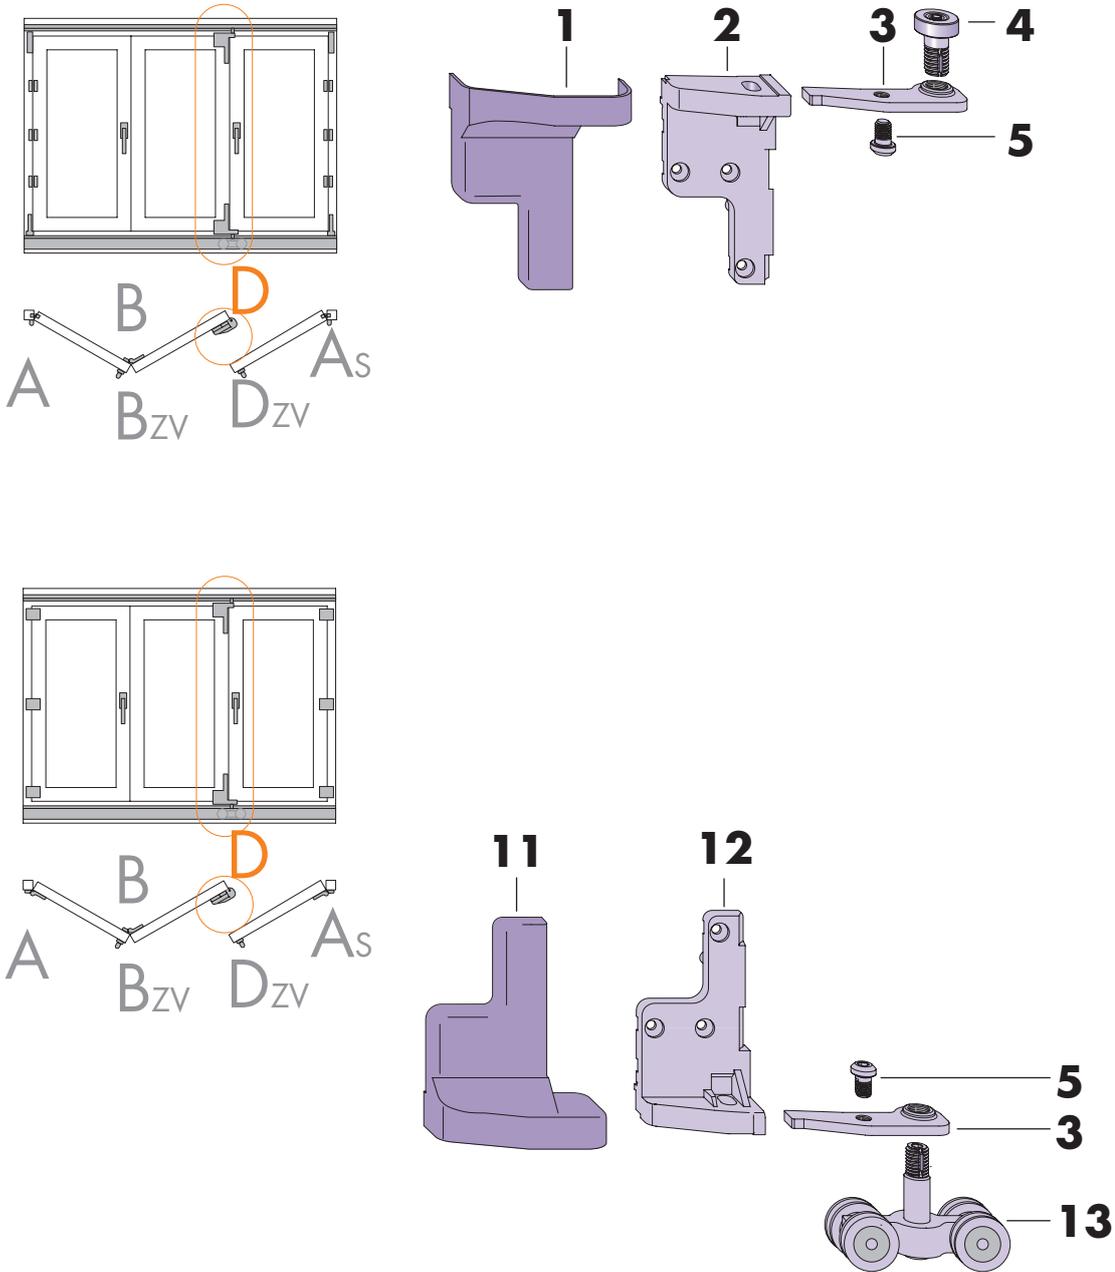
Beschlagabbildung Schnittpunkt D - Holz/ Kunststoff Elemente barrierefrei innenlaufend
